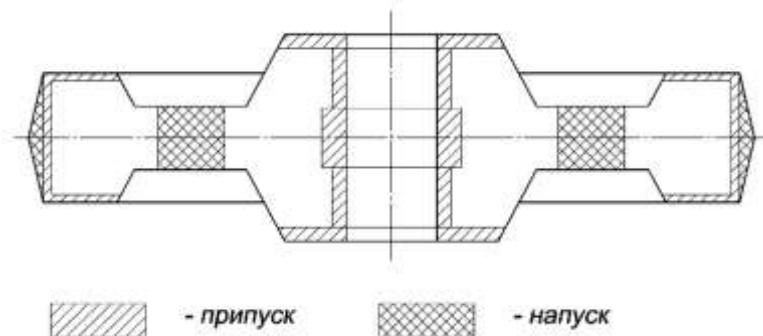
Припуски на обробку та напуски заготовки
